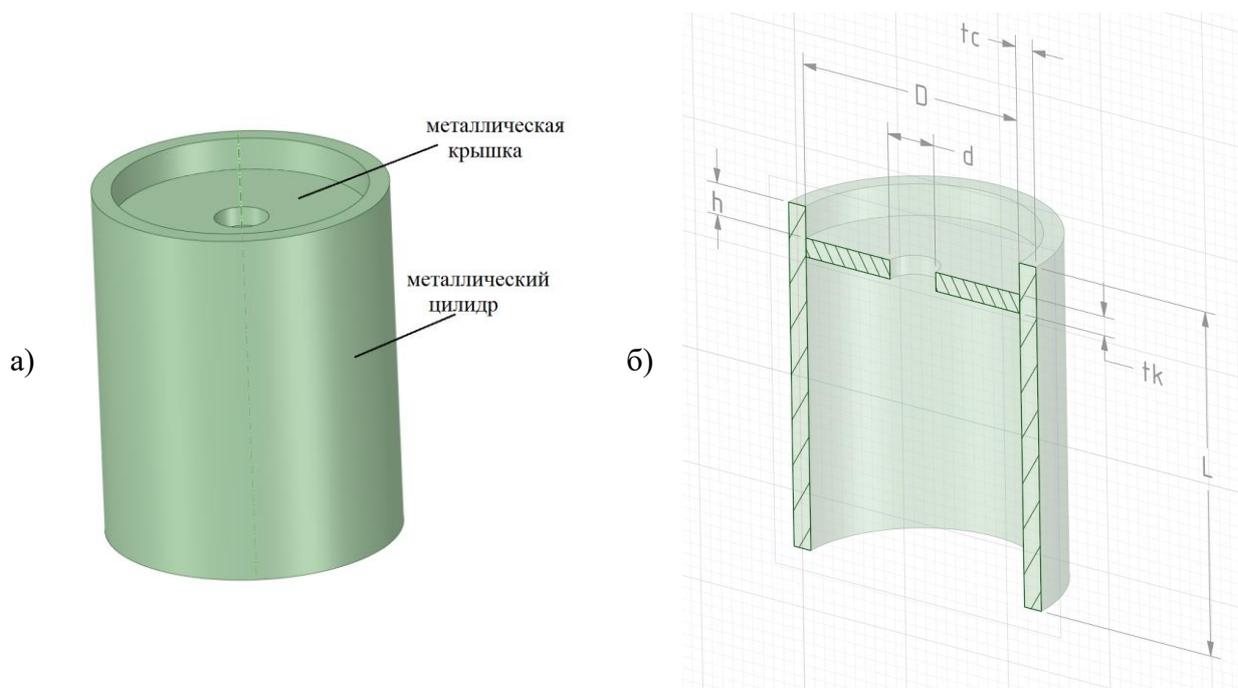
а) общий вид модели цилиндра с крышкой;
